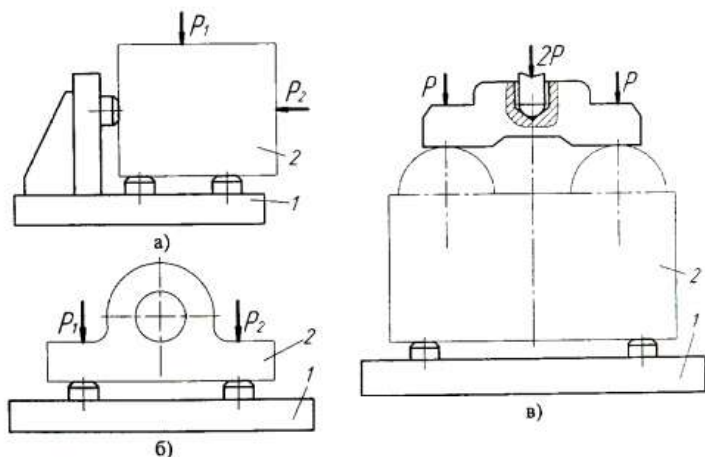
Узагальнені схеми закріплення заготовки у пристрої: 1 – пристрій; 2 – заготовка
